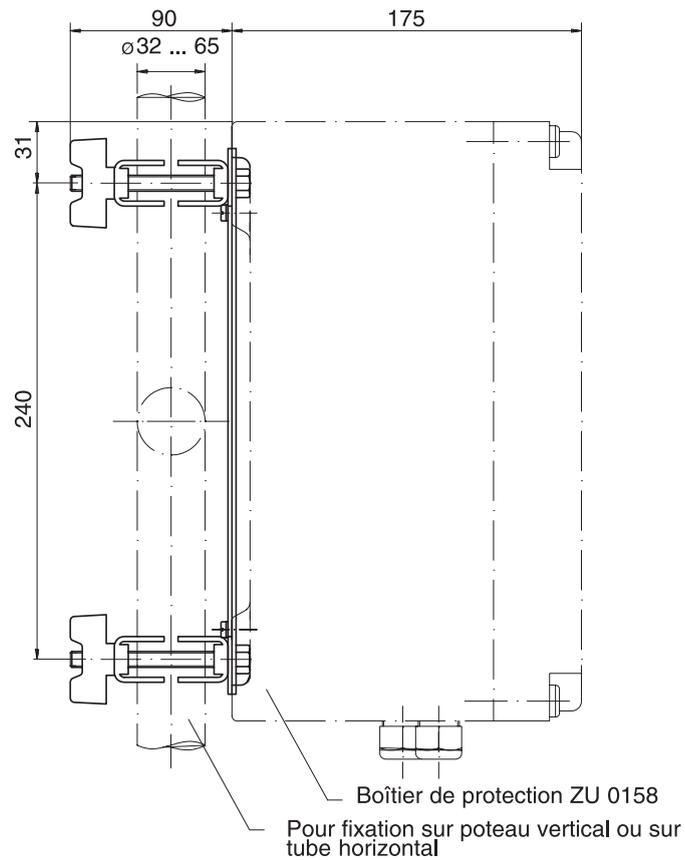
Jeu de colliers pour fixation sur mât ZU 0220 pour boîtier de protection ZU 0158
